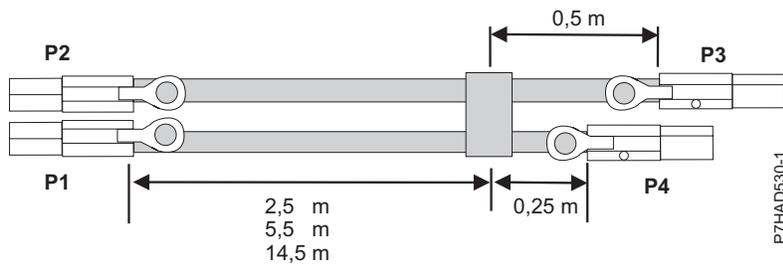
Longitudes de cable de conjunto de cables X SAS externos
